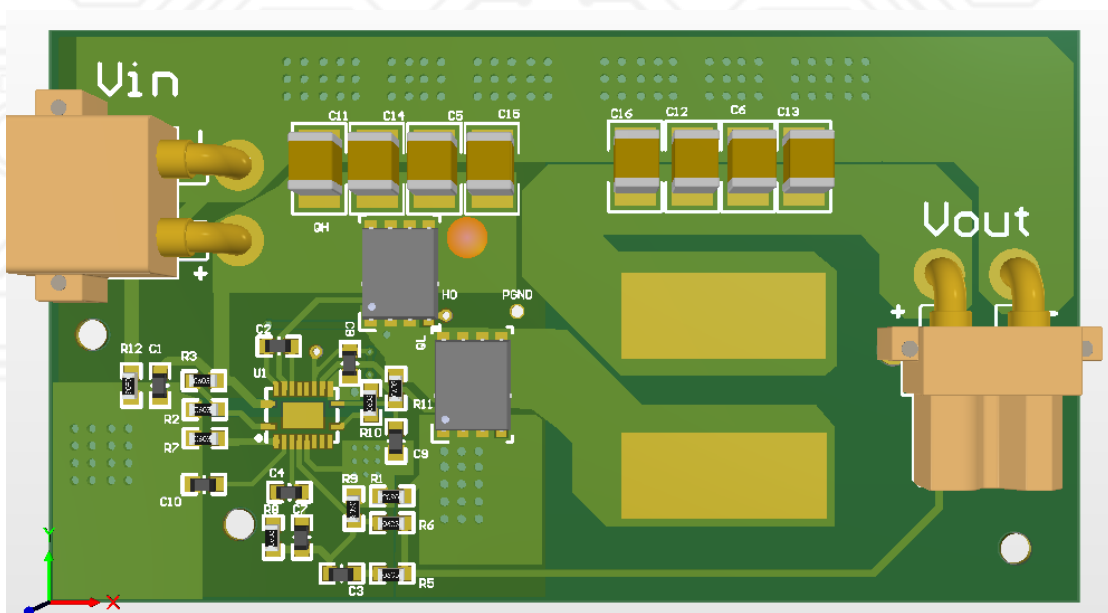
2022 赛季 48V 转 24V 稳压模块 PCB
